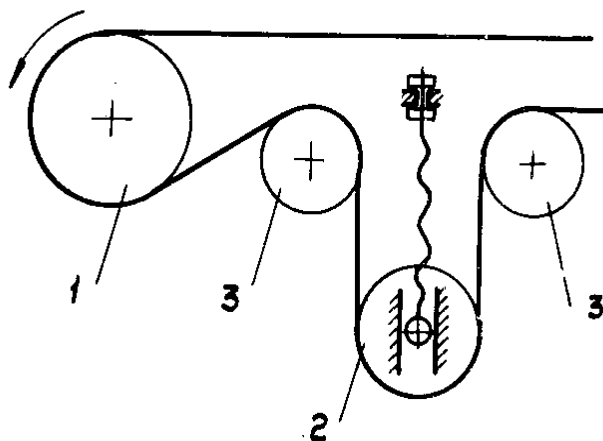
Схема натяжного пристрою, розташованого біля приводного барабана: 1 – приводний барабан; 2 – натяжний барабан; 3 – відхиляючий барабан
